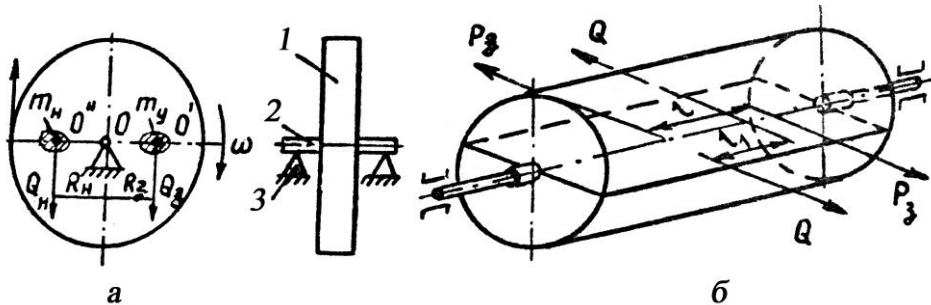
Схема врівноваження деталей під час балансування: а — статичного; б — динамічного; 1 — деталь; 2 — оправка; 3 — опора
